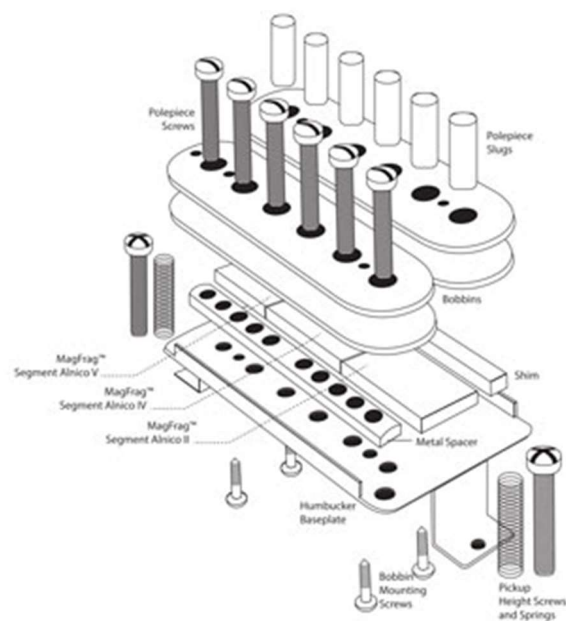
Despiece de una pastilla Doble o Humbucker por Seymour Duncan
